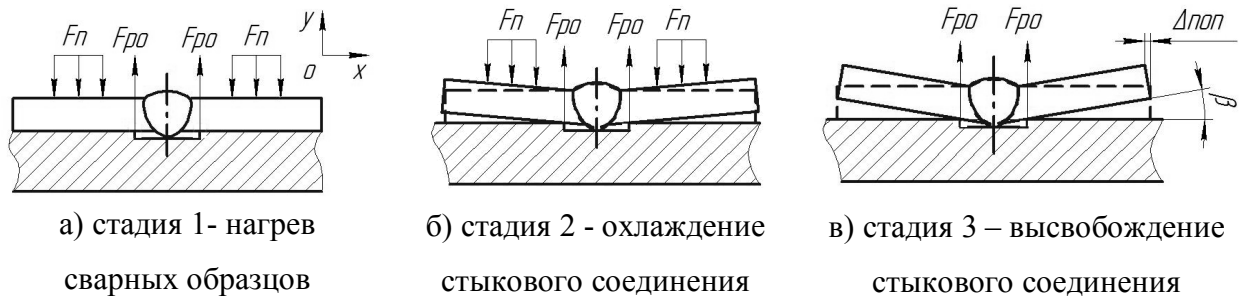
Схемы закрепления стыкового соединения из плоских образцов в процессе сварки и охлаждения
